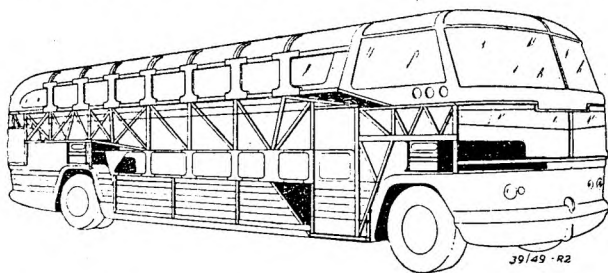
Widok piętrowego autobusu dalekobieżnego „The Greyhound Highway Traveler”.
